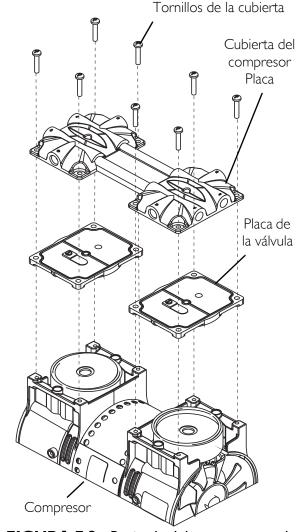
Retirada del compresor y de las cubiertas del compresor - Reconstrucción del compresor - Compresor - Placa de la cubierta del compresor - Placas de la válvula
